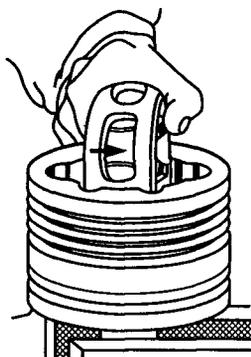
Извлечение сепаратора в сборе с обоймой из корпуса шарнира (стрелкой показано удлиненное окно сепаратора)
